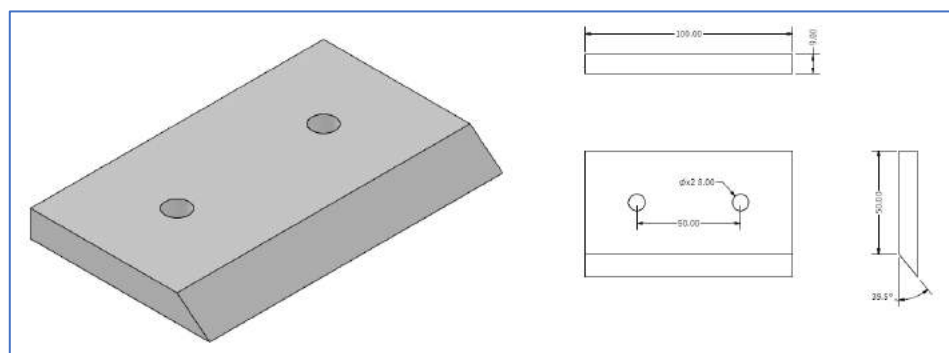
Dimensiones de la cuchilla de corte con ángulo de corte de 39.5°
